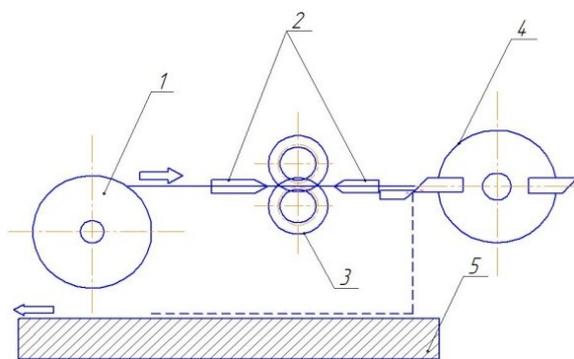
Схема нарезки стальных фибровых элементов: 1 – бухта проволоки; 2 – направляющие; 3 – профилирующие вальцы; 4 – режущая головка; 5 – бетонируемая поверхность
